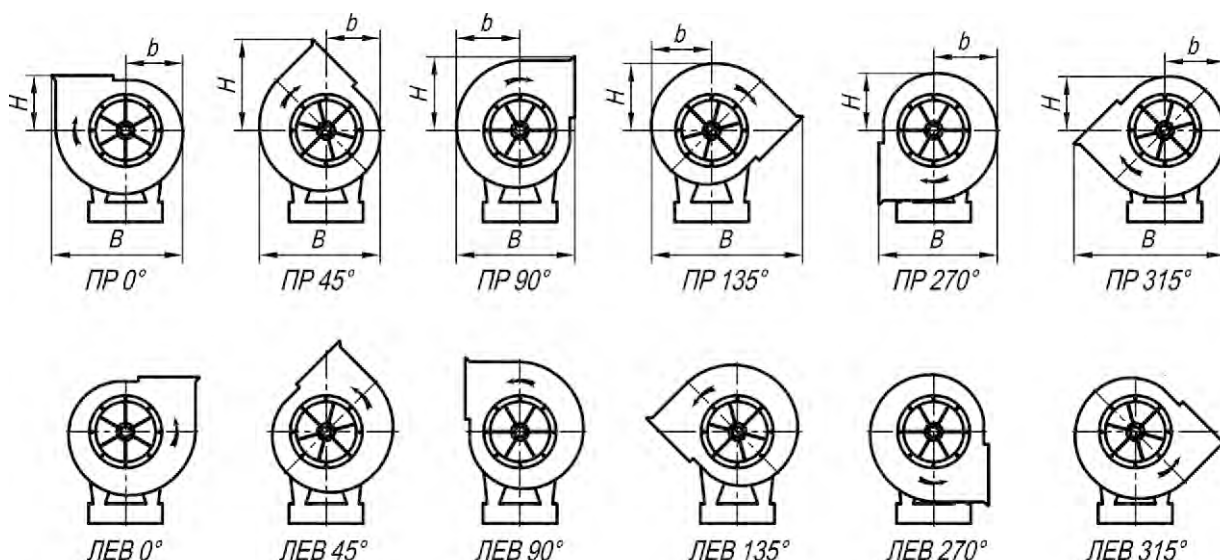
Положение корпуса вентилятора ВР 140-40 исп-1.
